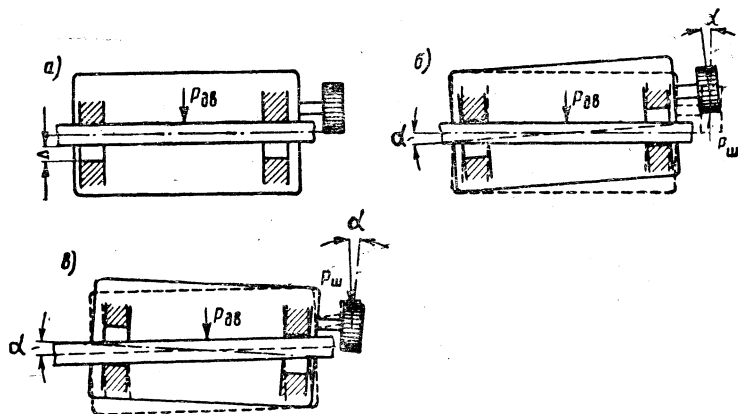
Схемы наклона зубьев шестерен при наличии зазоров в моторно-осевых подшипниках:
